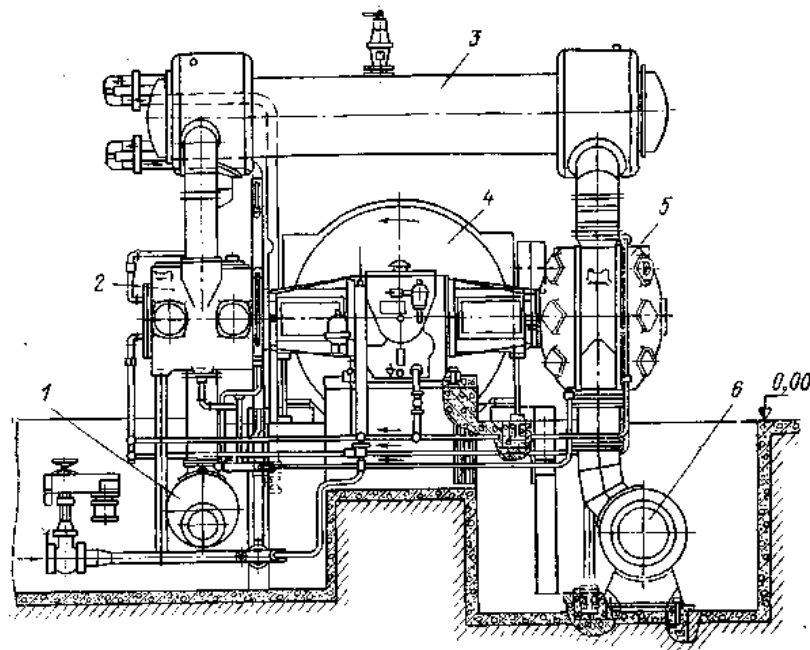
Конструкція поршневого компресора 4VM10-100/8
